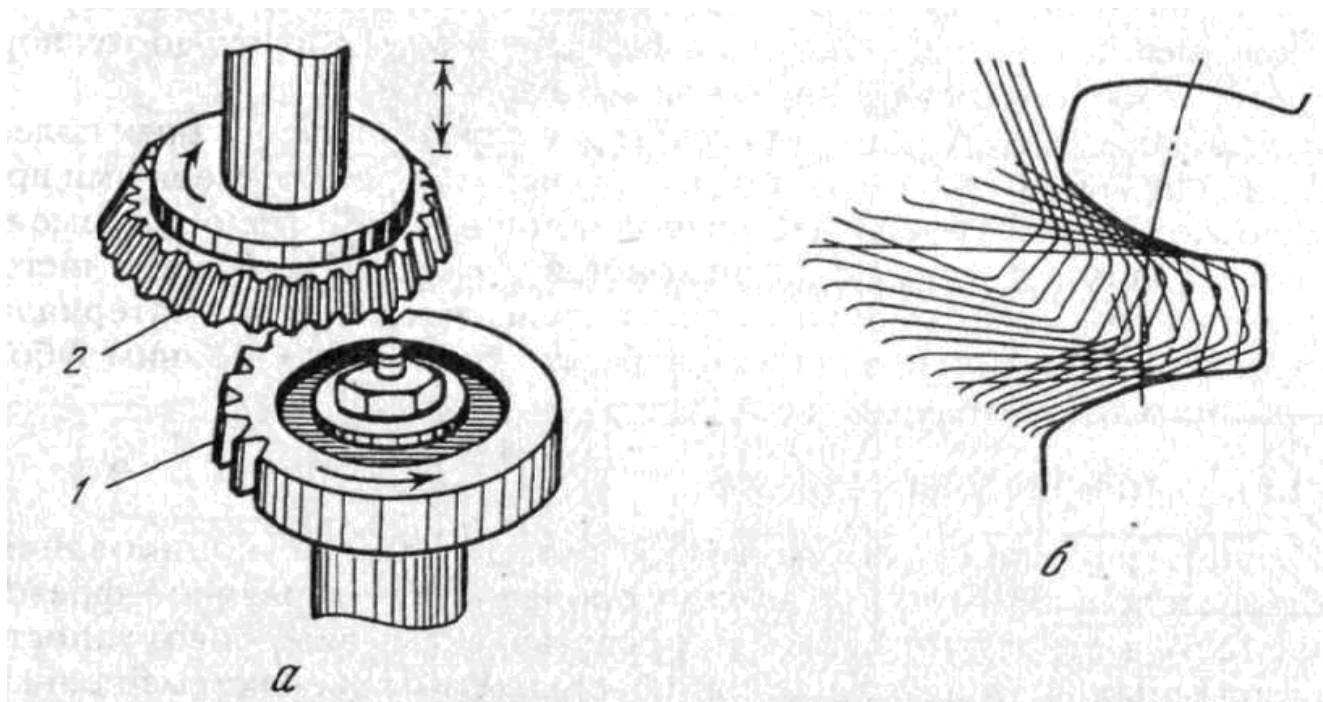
Схемы нарезания зубчатых колес методом обката: а - долбяком, б – червячной фрезой.
